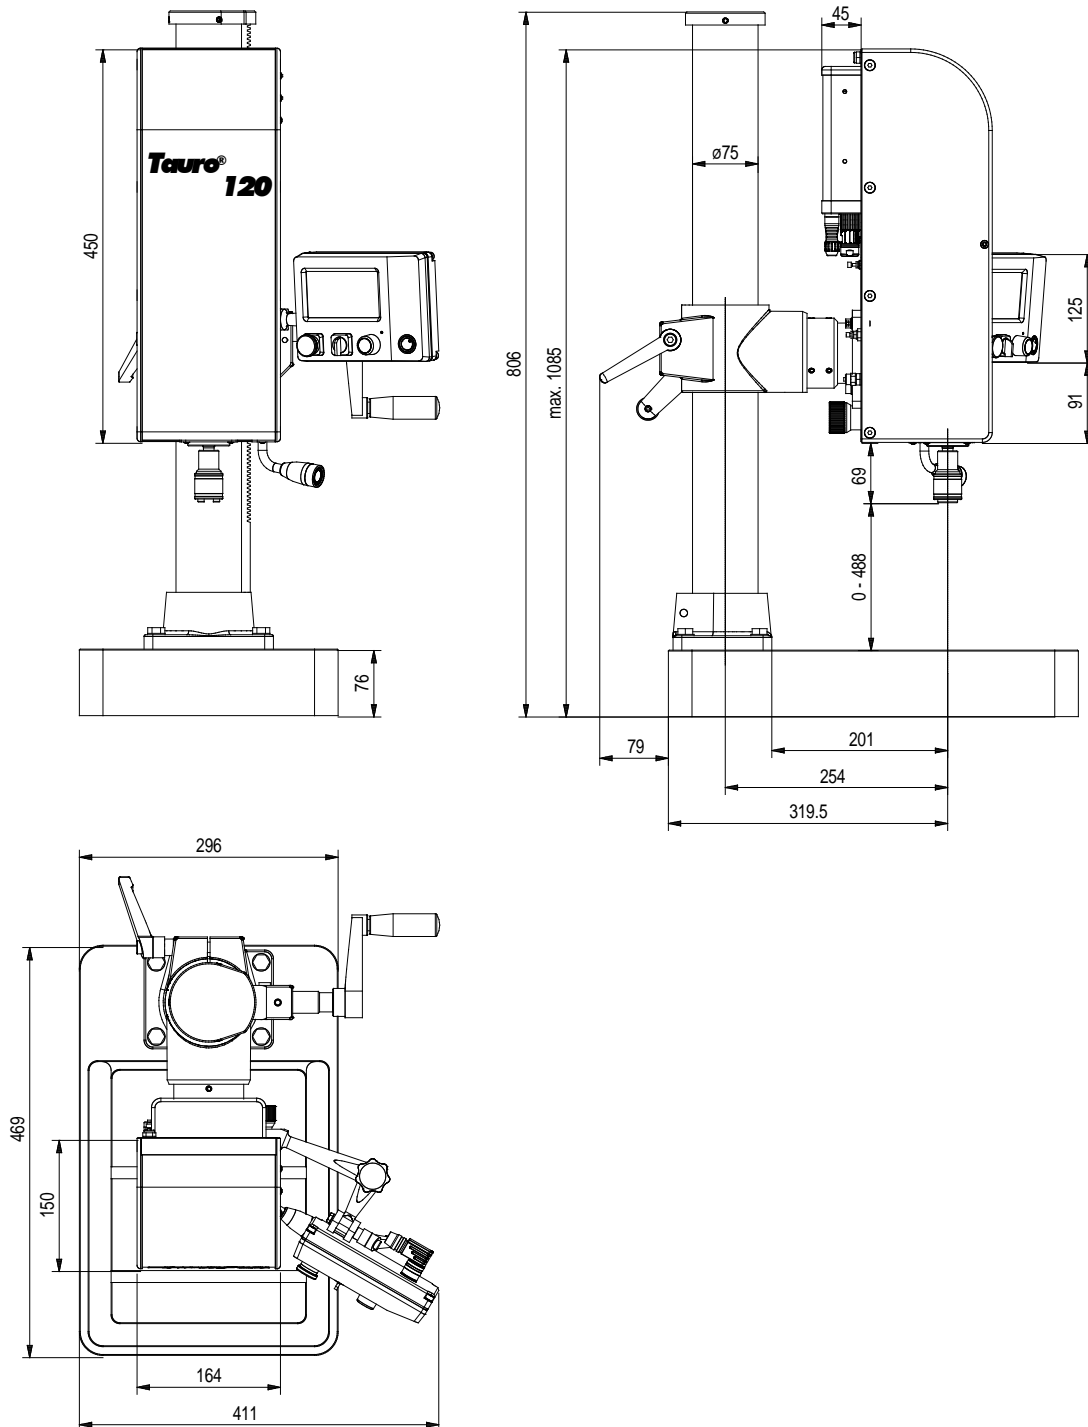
Ansichten der Gewindebearbeitungseinheit Tauro 120
